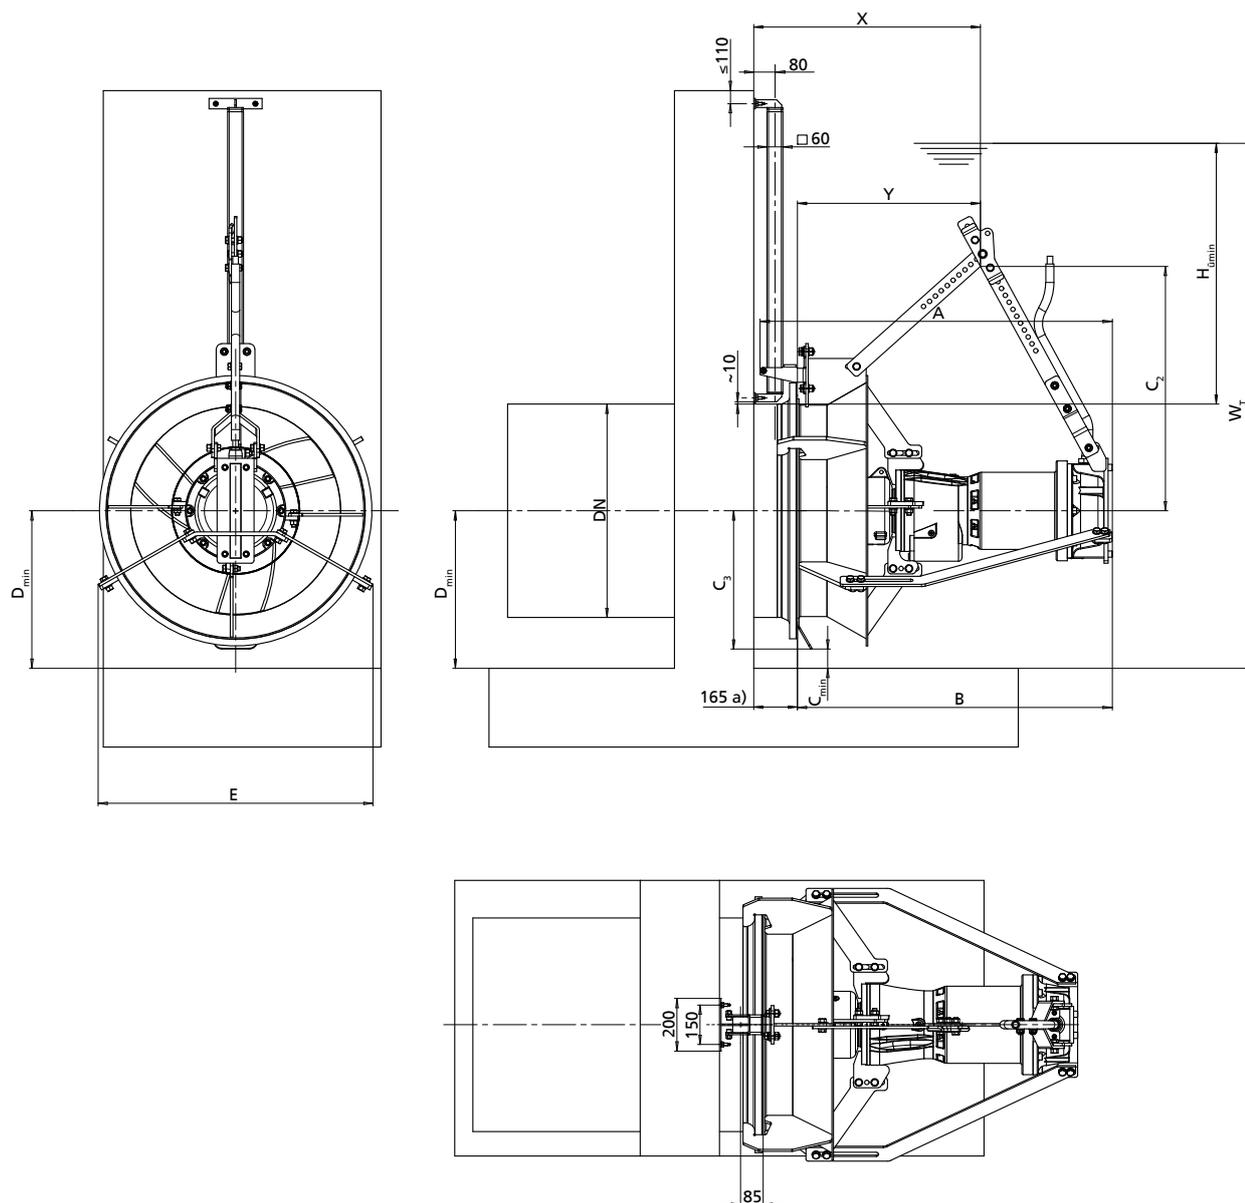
Габаритные размеры Amaline 500, 600, 800 - материал корпуса двигателя – серый чугун
